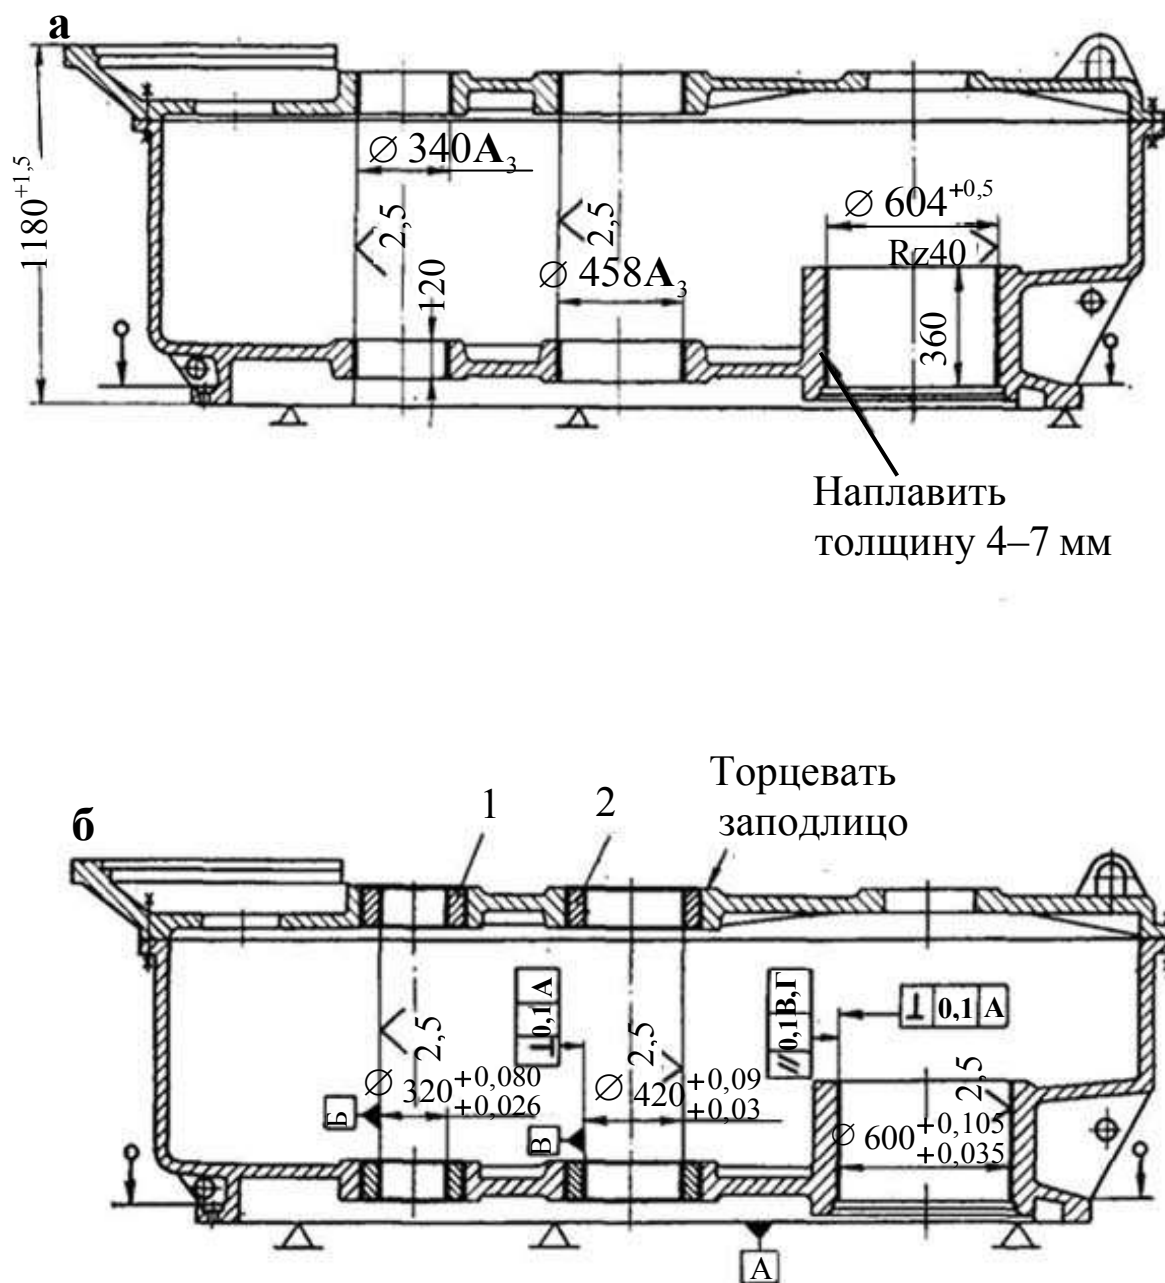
Ремонтные чертежи корпуса и крышки редуктора поворотного механизма: а – предварительной расточки отверстий; б – запрессовки втулок и чистовой расточки отверстий
